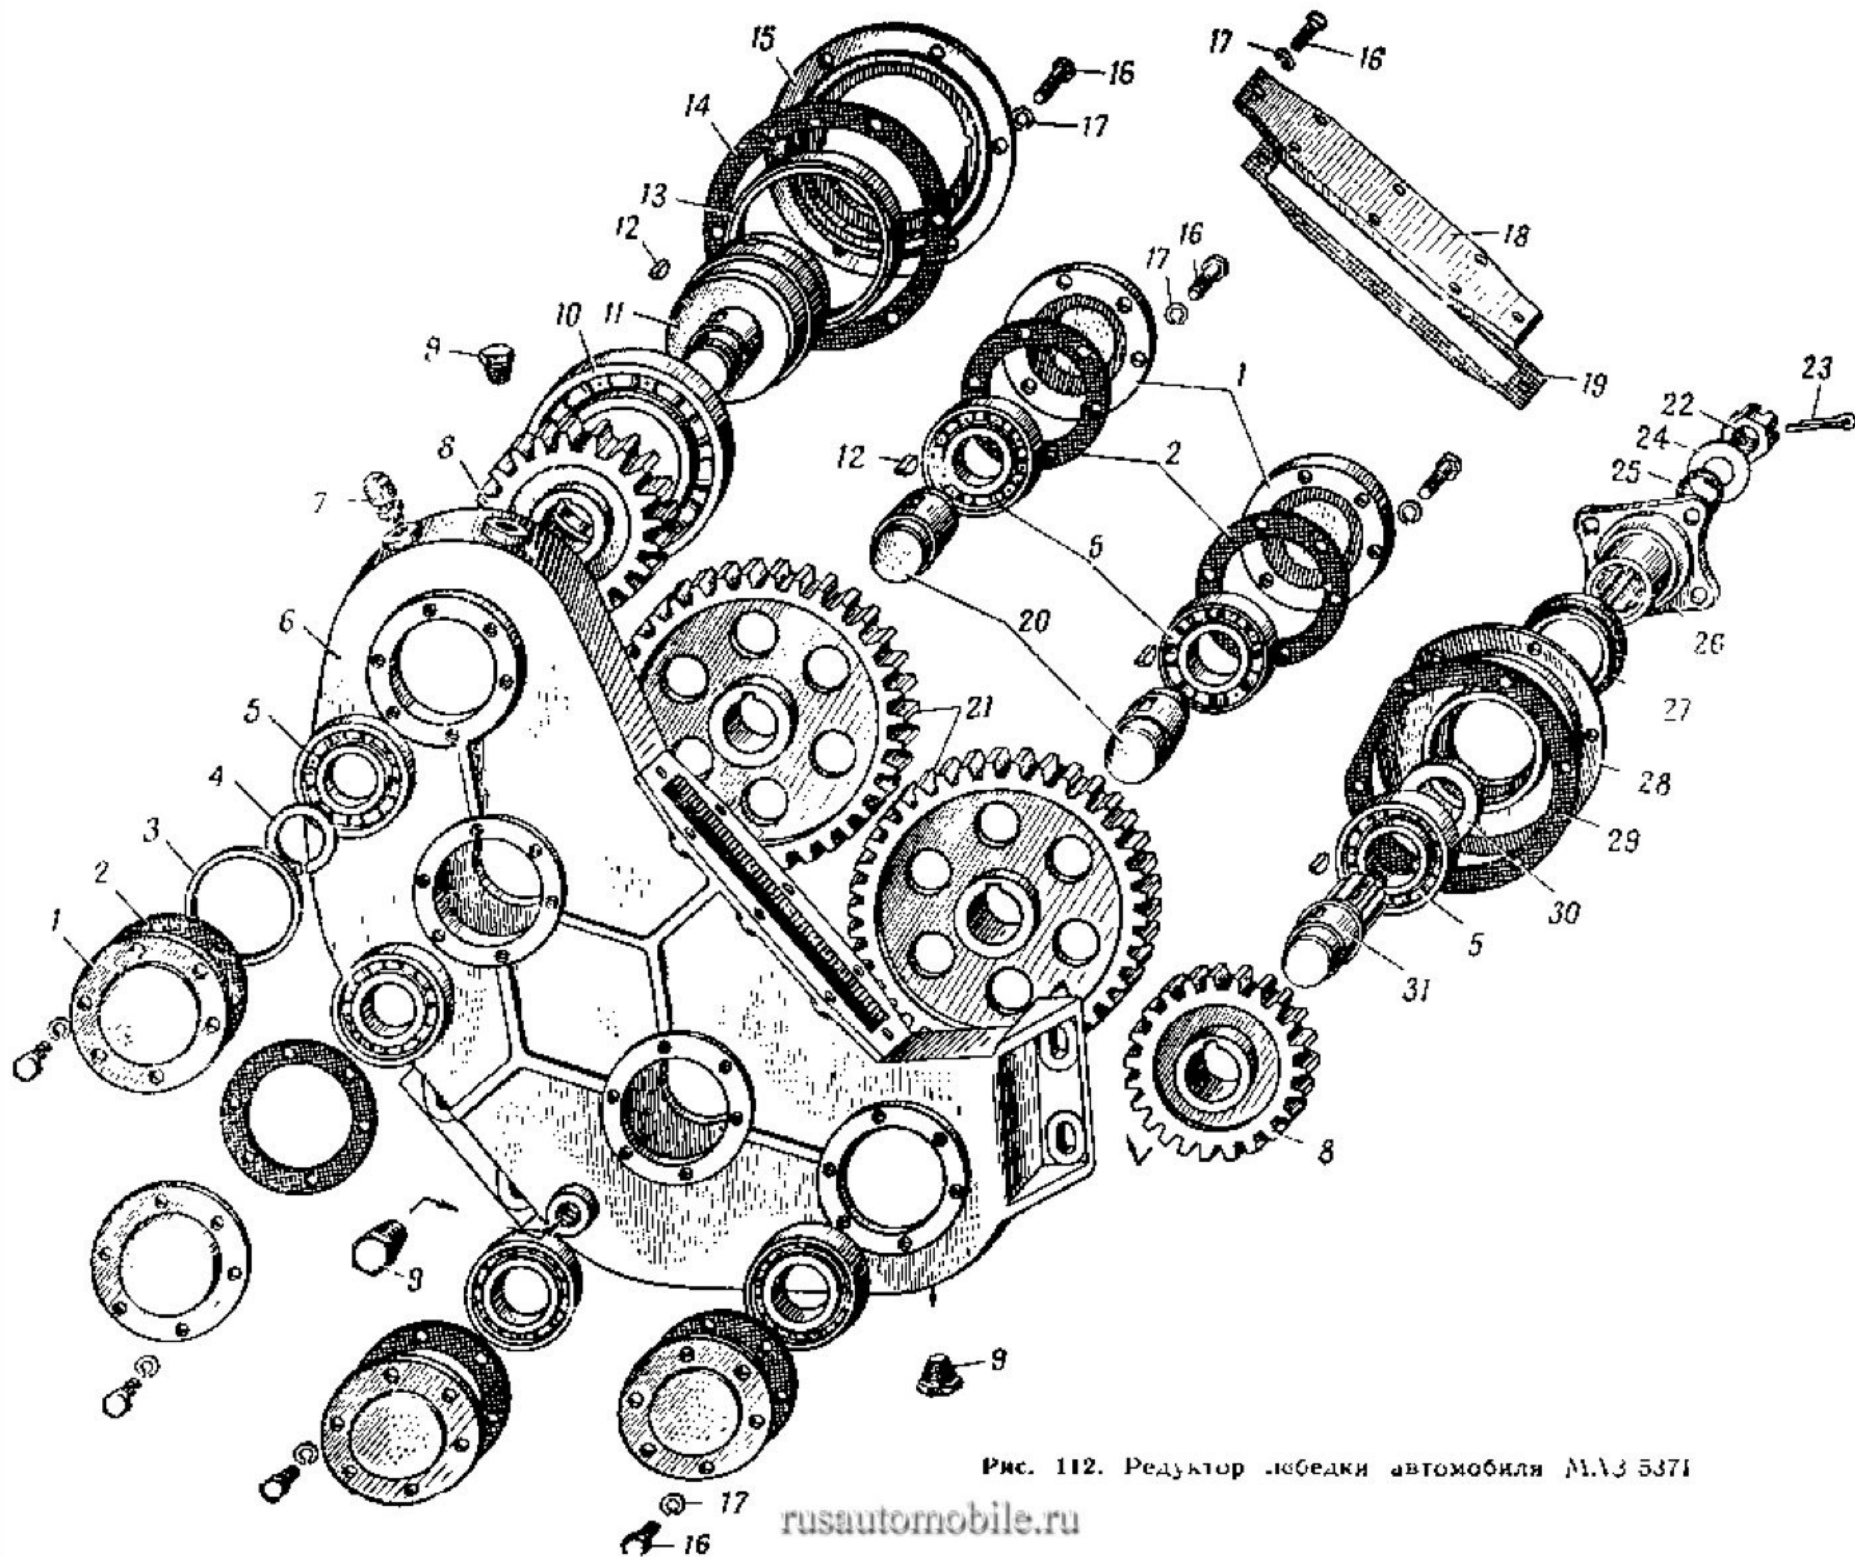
Редуктор сцепки автомобиля МАЗ 5371
